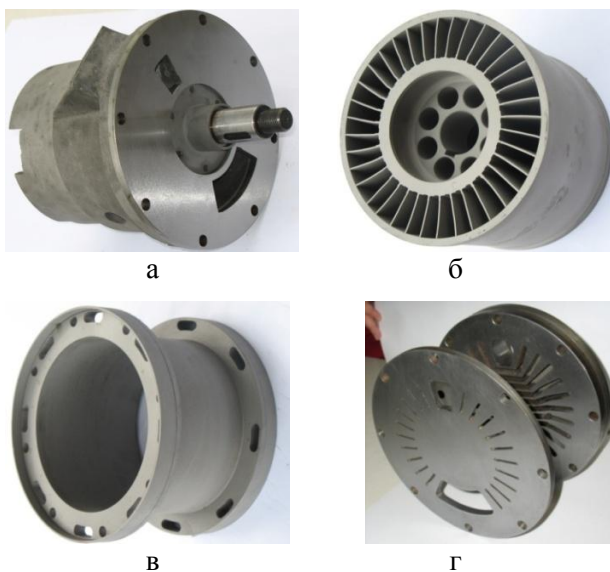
Основные элементы конструкции опытного образца КОД: а – статор; б – ротор; в – корпус; г – торцевая крышка со стороны подвода и отвода сжимающего газа
